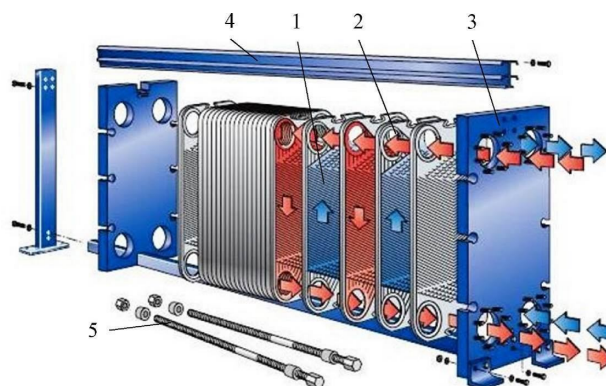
Конструктивні схеми пластинчатого теплоутилізатора: 1 – робочі пластини; 2 – гумові прокладки; 3 – кінцеві камери з патрубками; 4 – рама; 5 – стяжні болти
